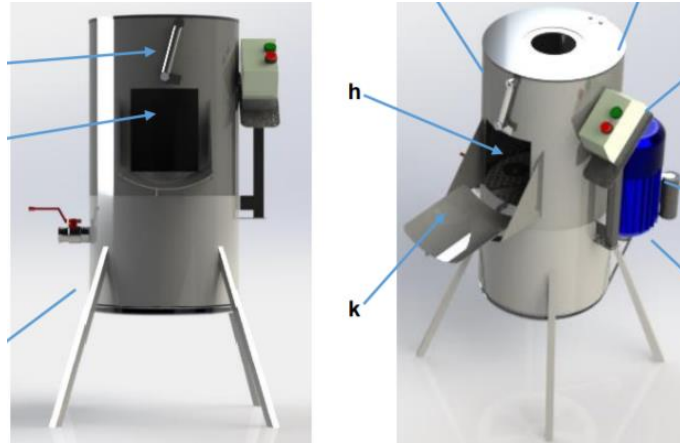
Vista frontal e isométrica de la máquina peladora de papa.
